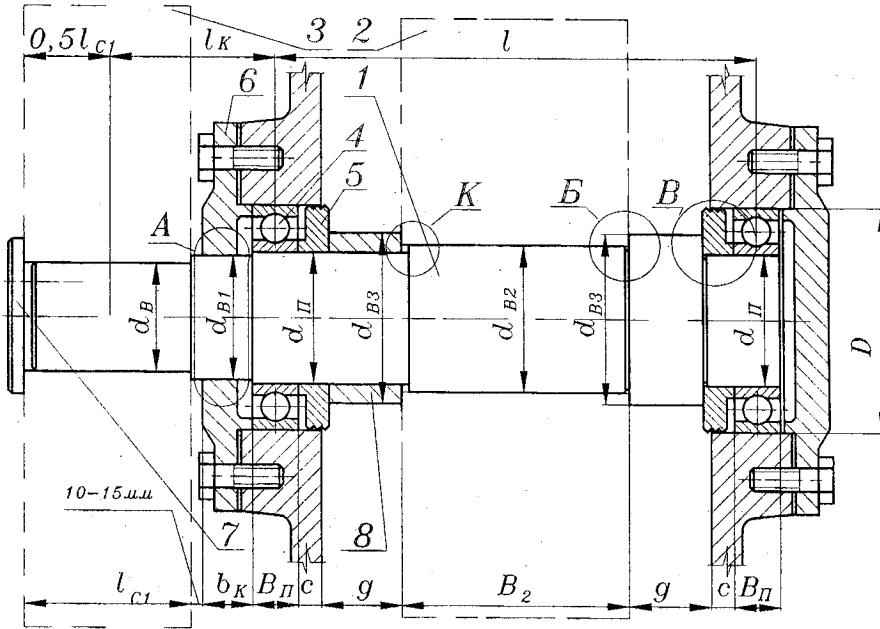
Ведений вал закритої прямозубої циліндричної передачі
